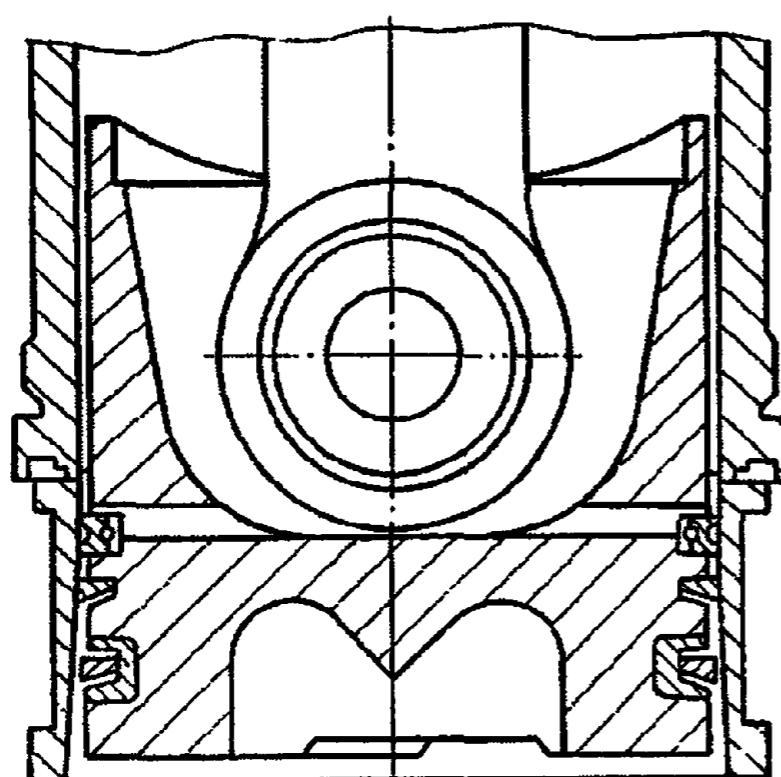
Приспособление И801.00.001-01 для установки поршня в гильзу цилиндра
